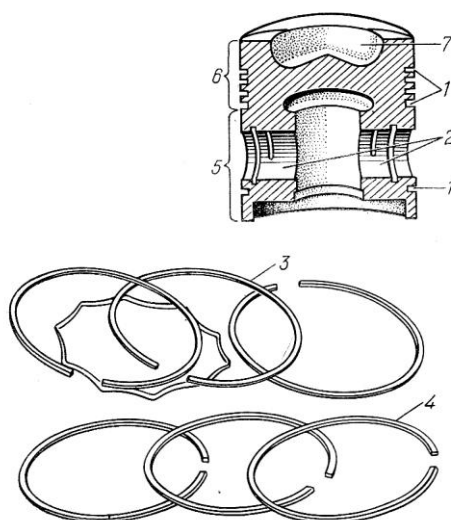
Поршень с поршневыми кольцами: 1 – канавки для поршневых колец; 2 – бобышки; 3 – маслосъемные кольца; 4 – компрессионные кольца; 5 – направляющая часть; 6 – уплотняющая часть; 7 – углубление
